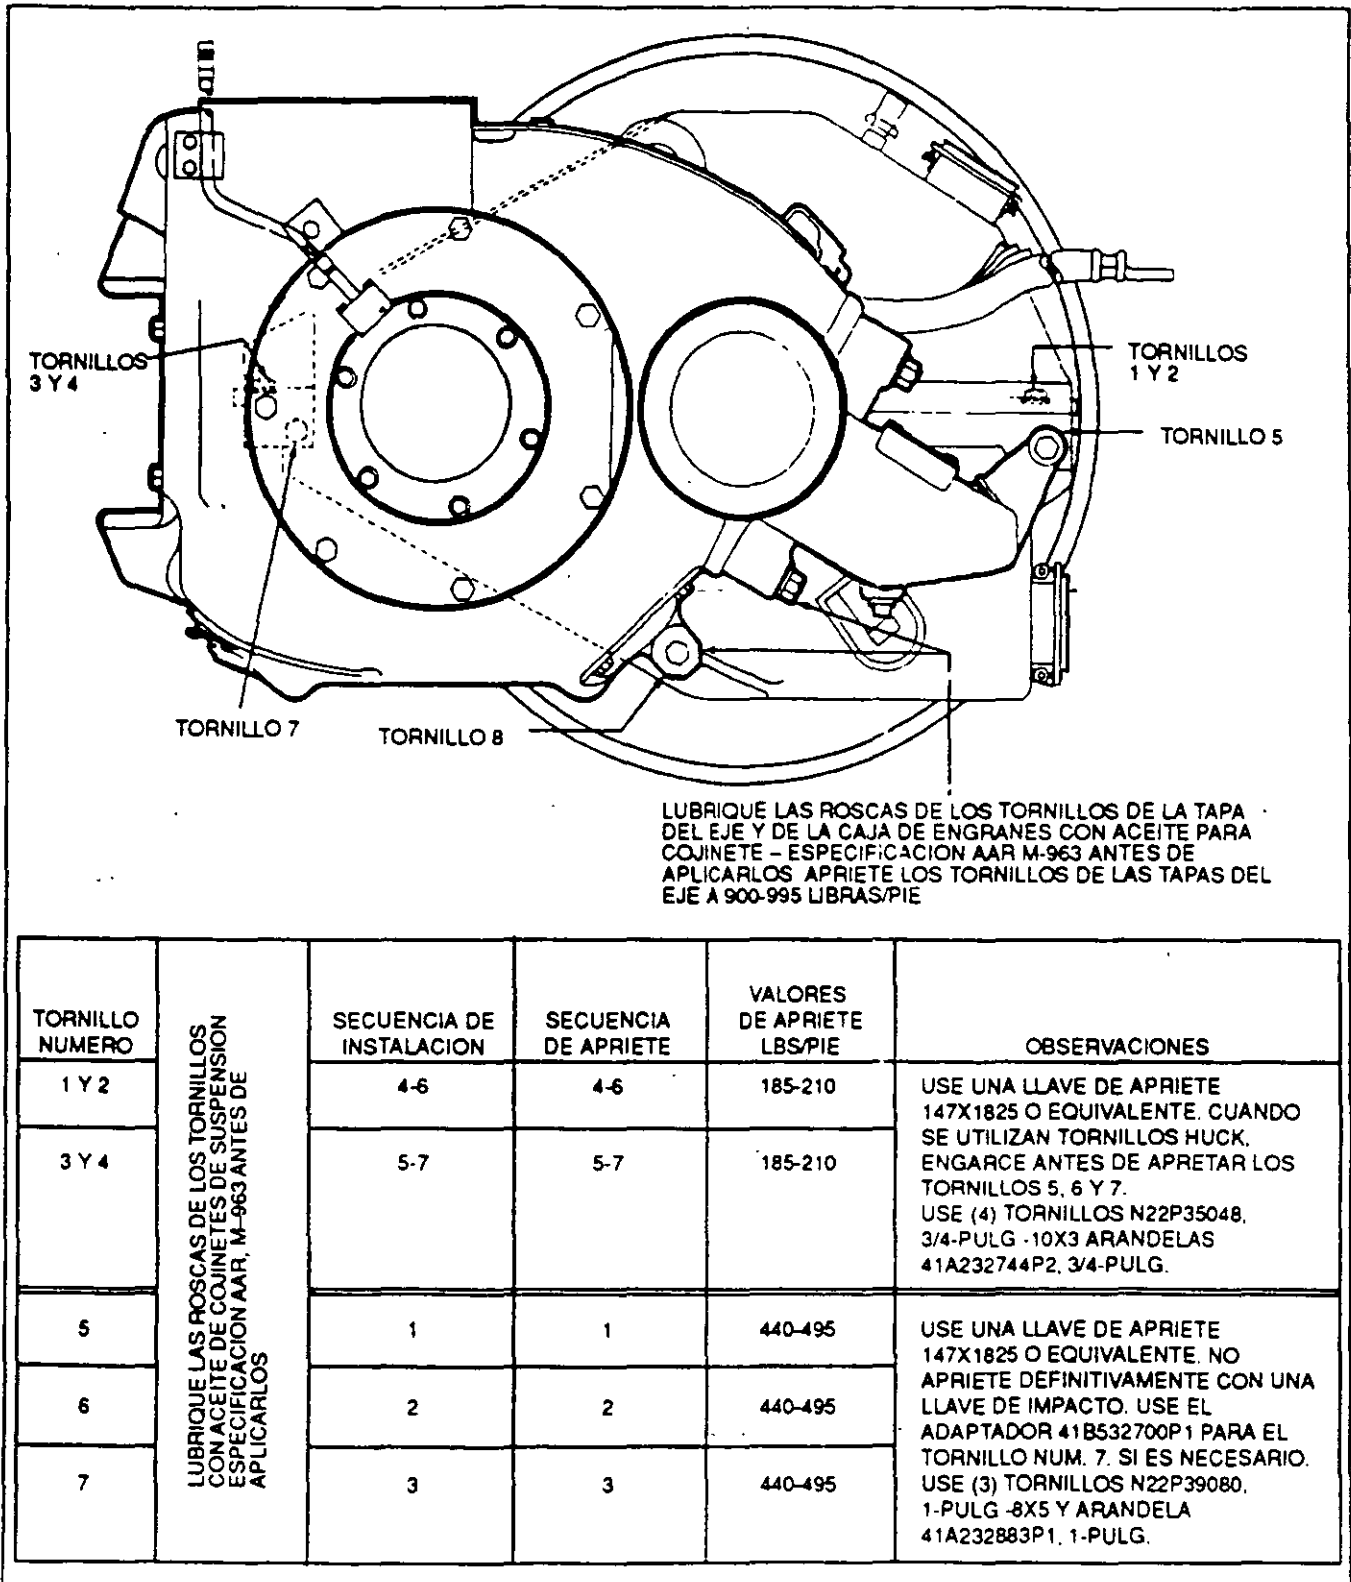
MONTAJE DE LA TAPA DEL EJE Y CAJA DE ENGRANAJES GE752AF. E-29369A-S
